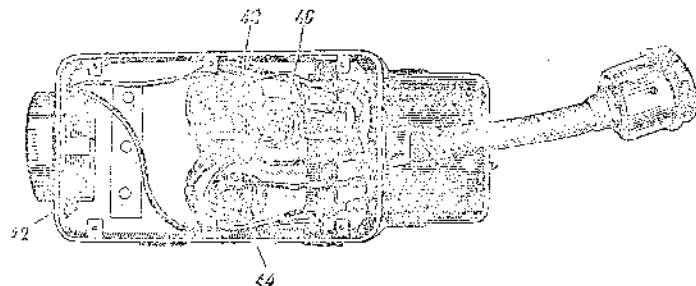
Фильтр умформеров РУК-300А и РУК-300В (обозначения см. на рис. 70)
